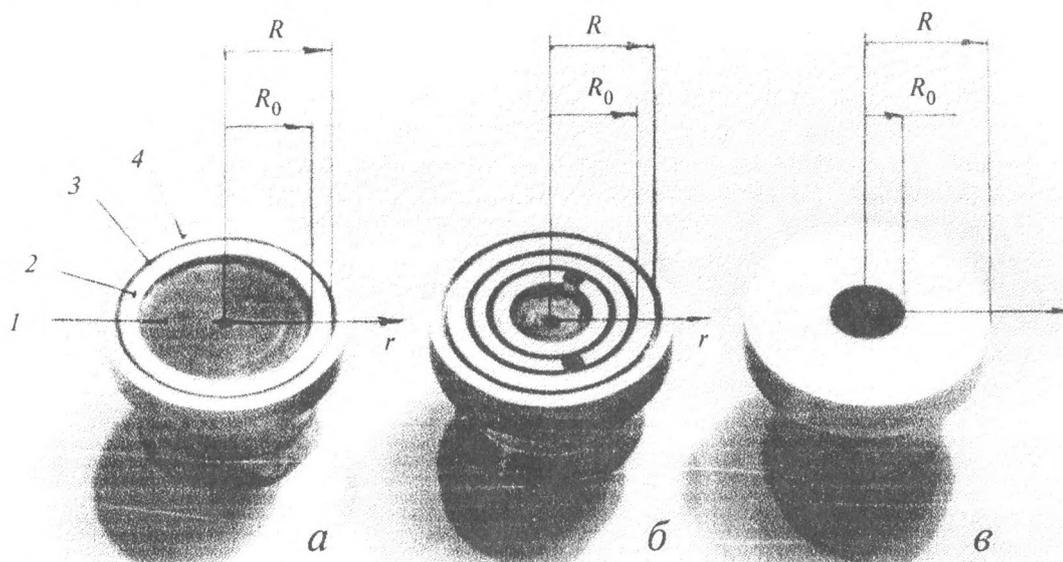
Скользящие поршневые гидростатические подпятники: а — с традиционной формой опорной поверхности: 1 — центральная расточка; 2 — уплотнительный поясок; 3 — дренажная канавка с каналами (сверление или паз) для “сброса” утечек; 4 — вспомогательный поясок (без гидростатического отжатия); б — с усложненной опорной поверхностью (с “лабиринтными” поясками); в — вид предлагаемого поршневого подпятника для серийных гидромашин
